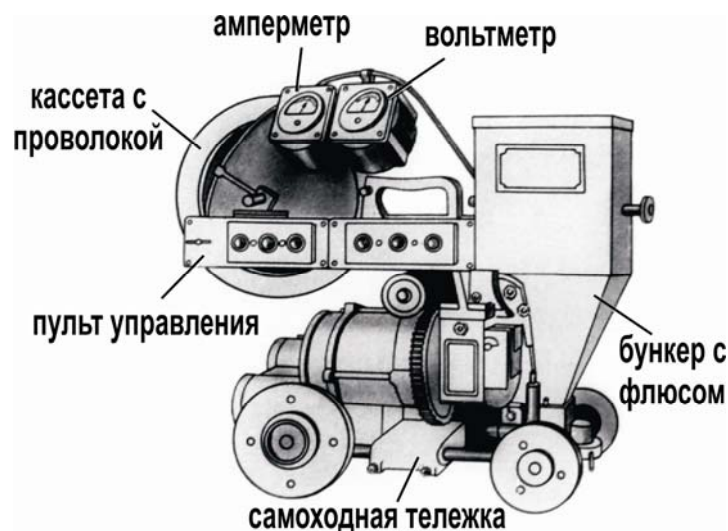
Общий вид самоходного сварочного трактора ТС-17 (АДФ-1002) для сварки под флюсом
